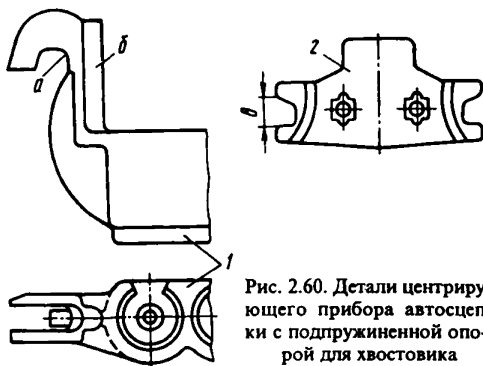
Детали центрирующего прибора автосцепки с подпружиненной опорой для хвостовика
